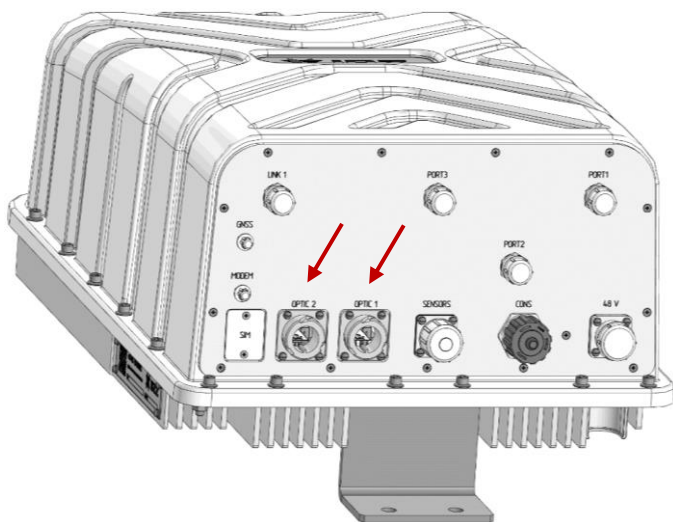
Установка корпуса для вилки и SFP+ в блок FSC или FSR1
